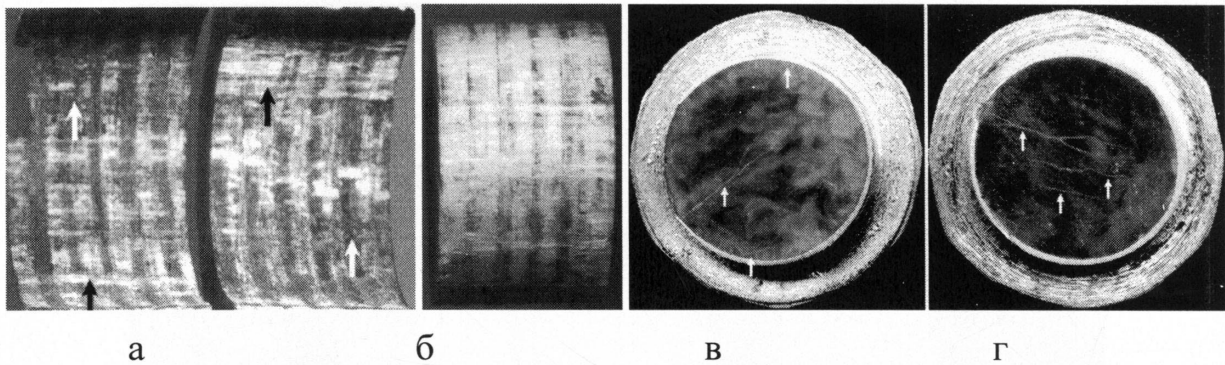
Вигляд деталей пресового з'єднання після двох років експлуатації: а – внутрішня поверхня головки; б – зовнішня поверхня стержня; в,г – розріз з'єднання (в – початок; г – середня частина)
